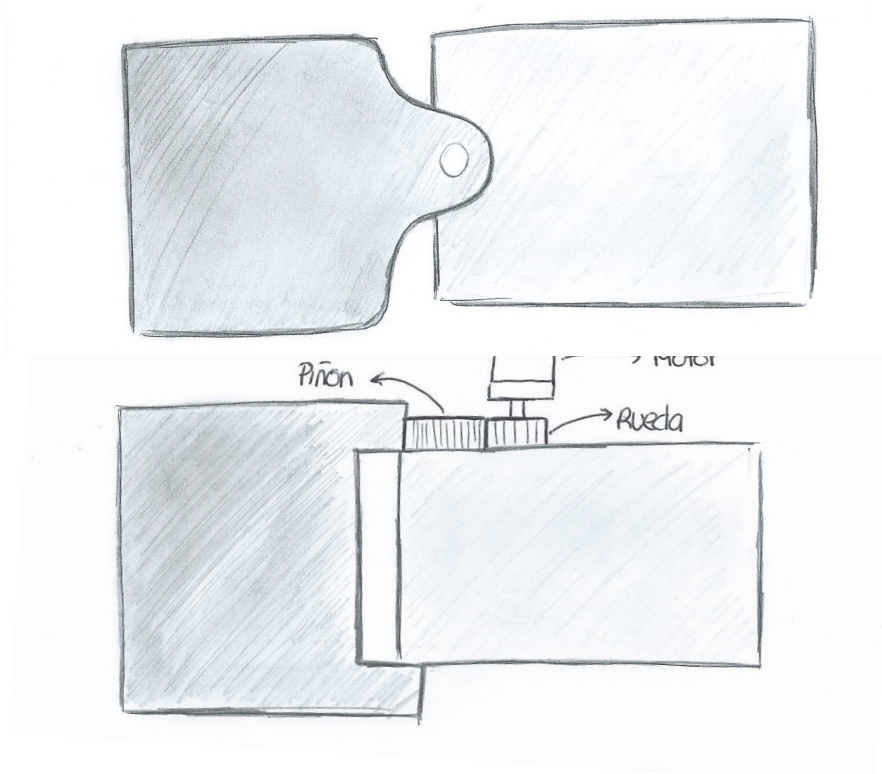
Segunda propuesta alzado y planta mecanismo; Fuente propia
